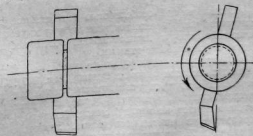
Схема фрезеровки зуба анкерного колеса.
